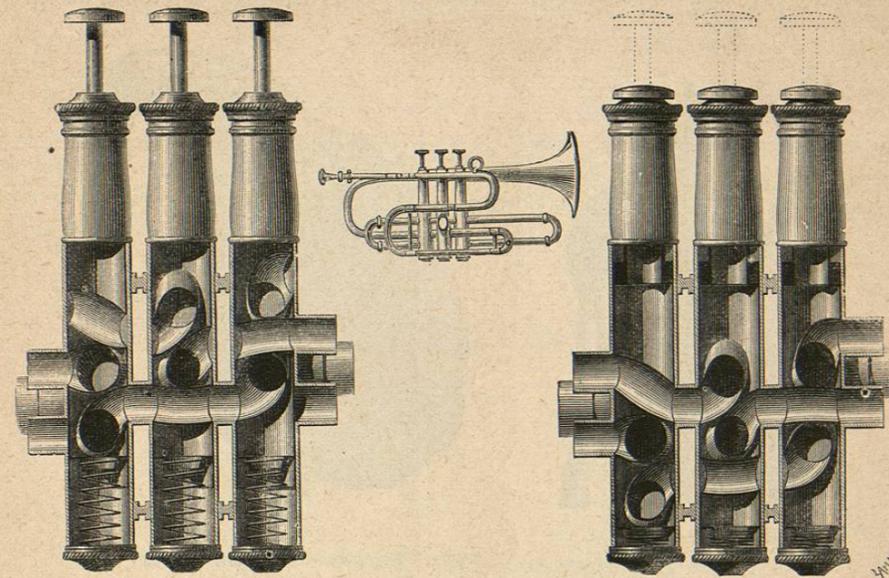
Cornetín: Corte de los pistones levantados y bajados
